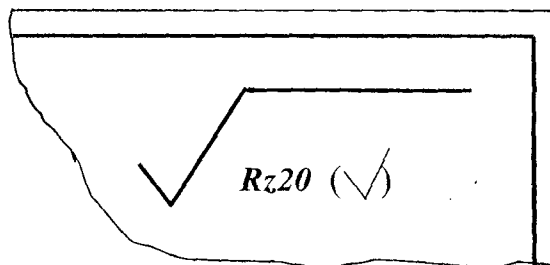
Примеры обозначений параметров одинаковой шероховатости
